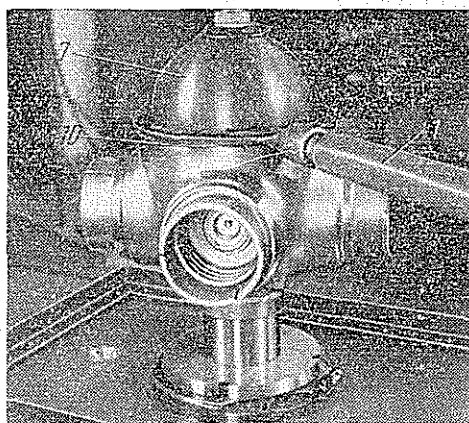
Вывертывание гайки цилиндра из корпуса:
